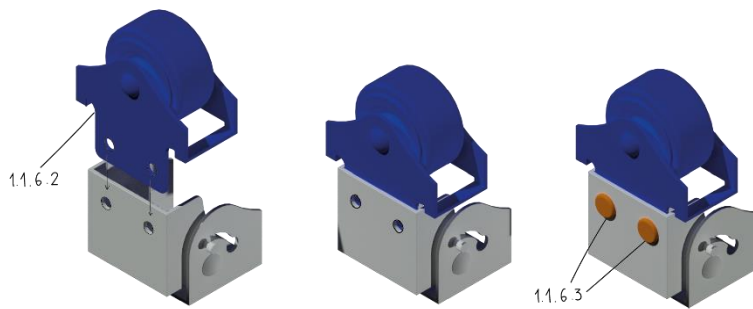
Ensamblaje subconjunto 1.1.6
